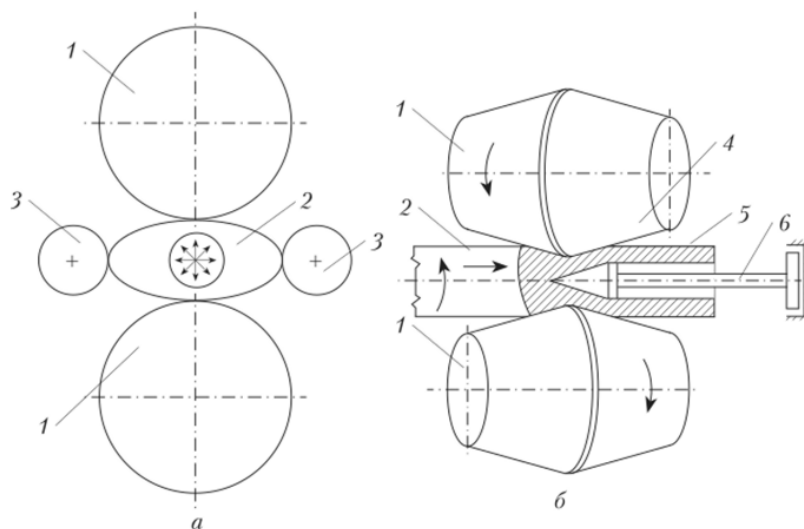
Поперечно-винтовая прокатка заготовки трубы (гильзы) [1]:
